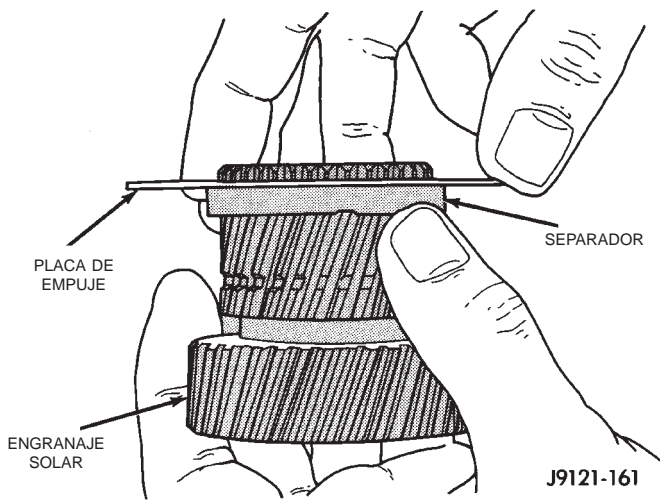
Instalación de la arandela de empuje delantera del casco impulsor en el engranaje solar
